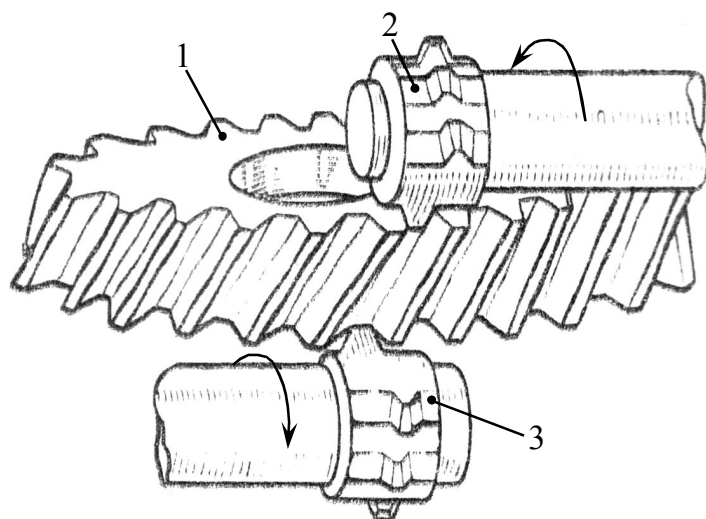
Схема двухстороннего снятия фасок косозубого цилиндрического колеса методом обката односторонней фрезой-улиткой:
